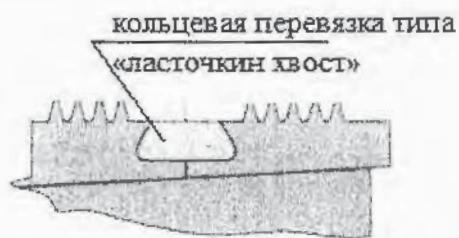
Цельнофрезерованные бандажи рабочих лопаток с кольцевой перевязкой типа «ласточкин хвост»
